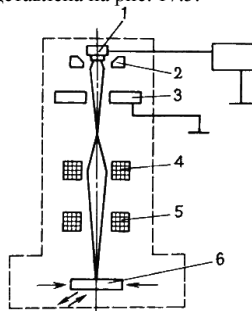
Схема установки для электронно-лучевой сварки
